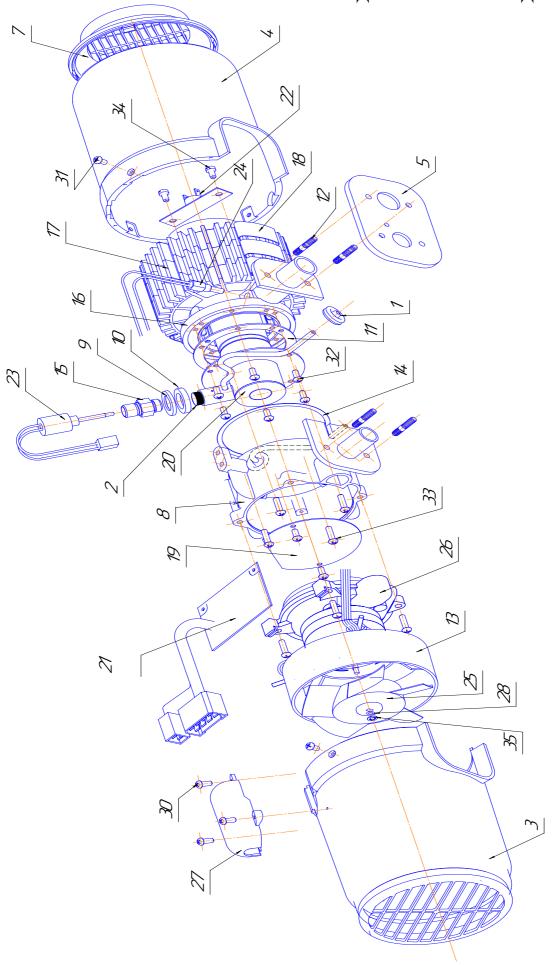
Схема деления нагревателя на составные части. (Нагреватель Сб.801 и нагреватель Сб.851 )
